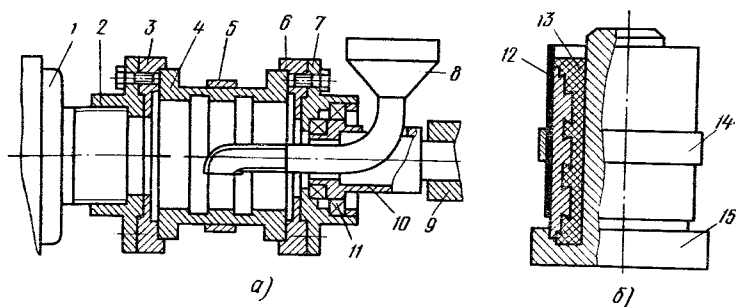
Приспособление для центробежной заливки (а) и форма для ручной заливки (б) вкладышей
